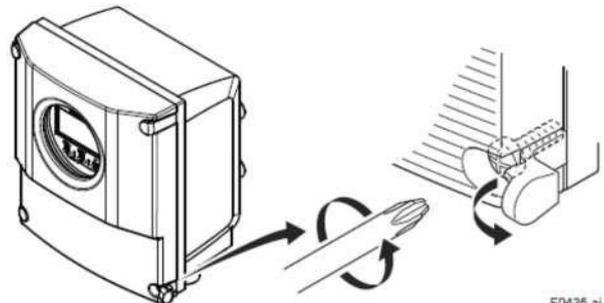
Remoção da Tampa Dianteira (Transmissor Remoto AXG1A)
